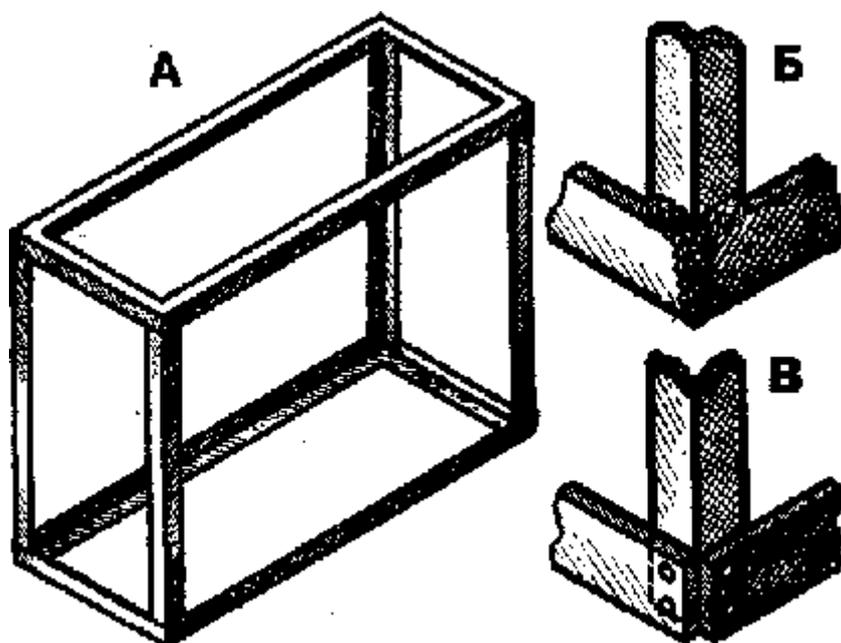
Каркас аквариума (А), со-единение уголков сваркой (Б) и заклепками (В)
